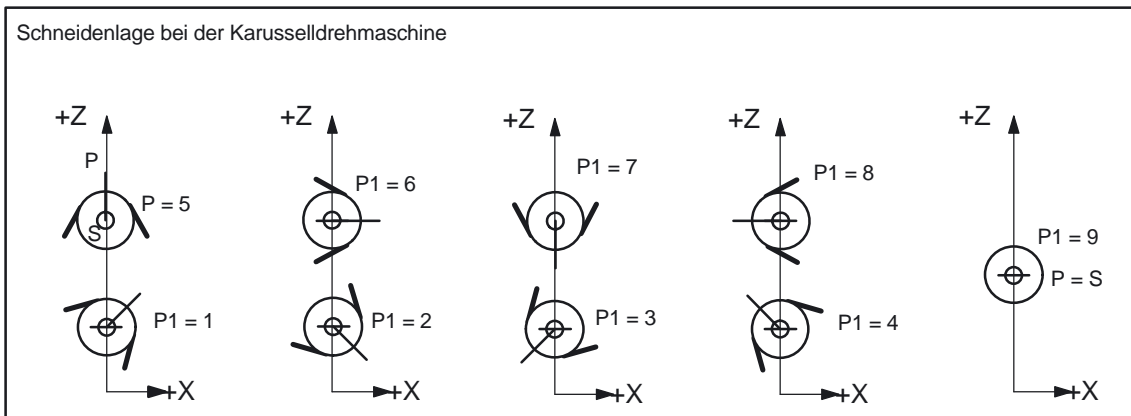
Definition der WZ-Schneidenlage bei Drehwerkzeugen
